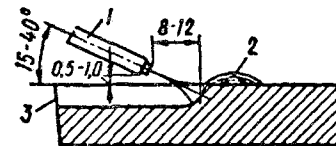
Схема поверхностной резки: 1 — мундштук; 2 — шлак; 3 — канавка
